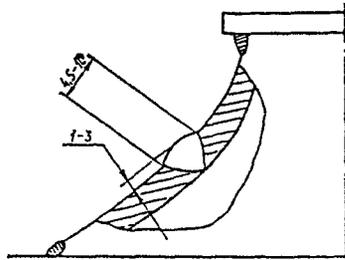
Размеры сварных швов на камере сгорания
